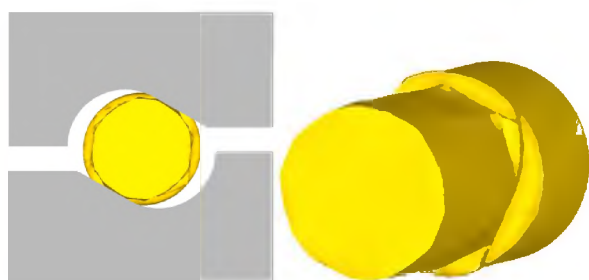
Форма заготовки послековки (протяжки) заготовок в бойках новой конструкции
